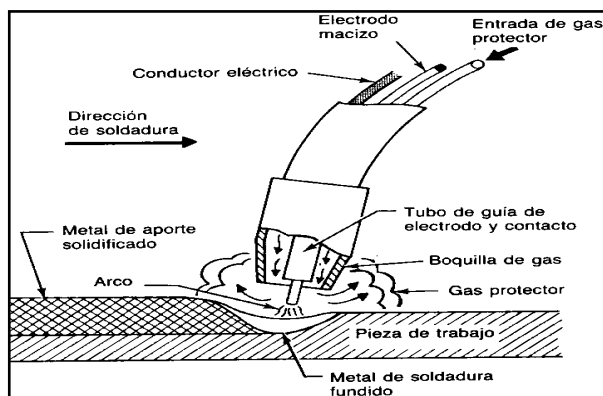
8 Ilustración de operación de proceso de soldadura *GMAW* (7).
